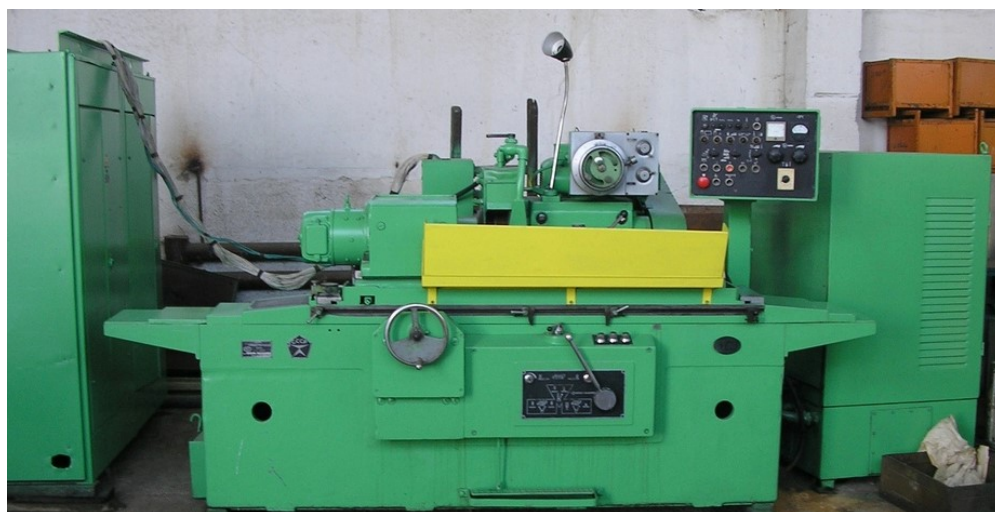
Круглошліфувальний верстат 3М151
